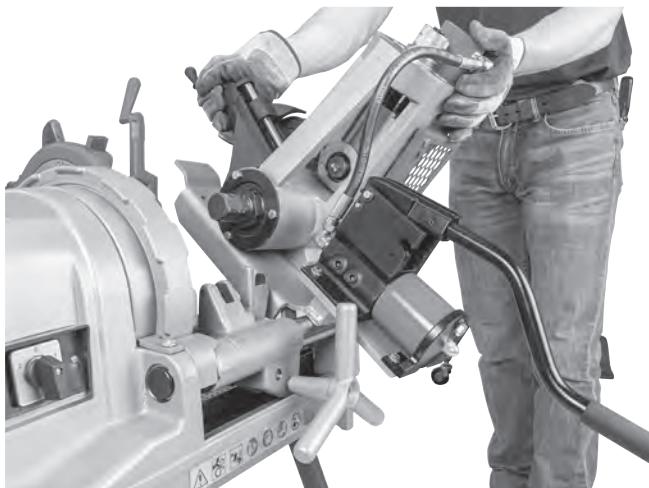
B – Installation der 918 an der Gewindeschneidmaschine 1233
